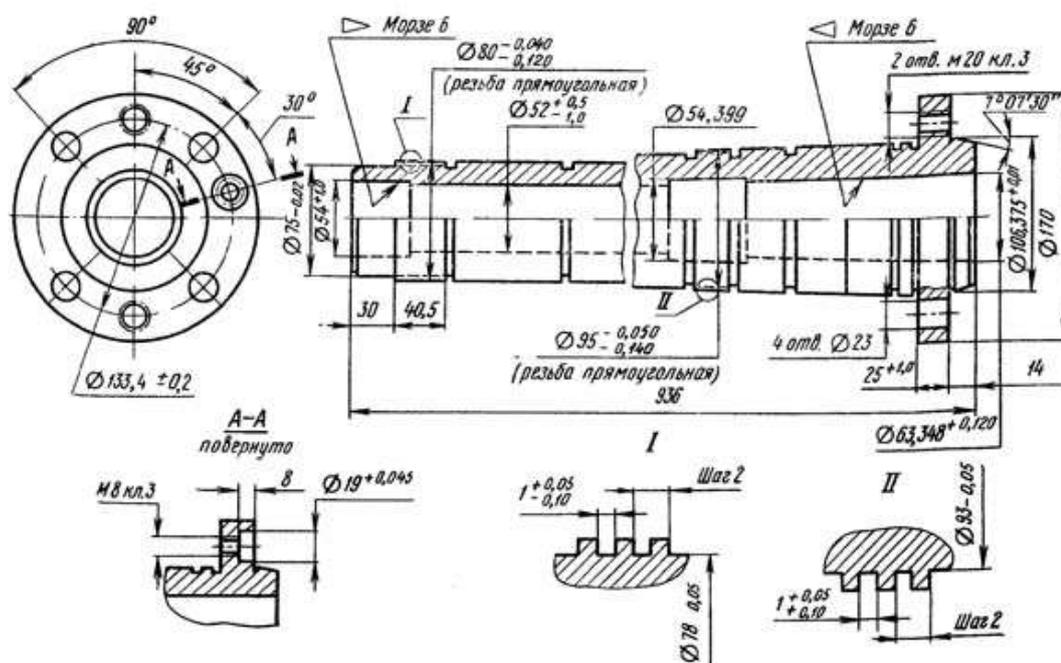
Конструкция шпинделя токарного станка мод. 16A20
